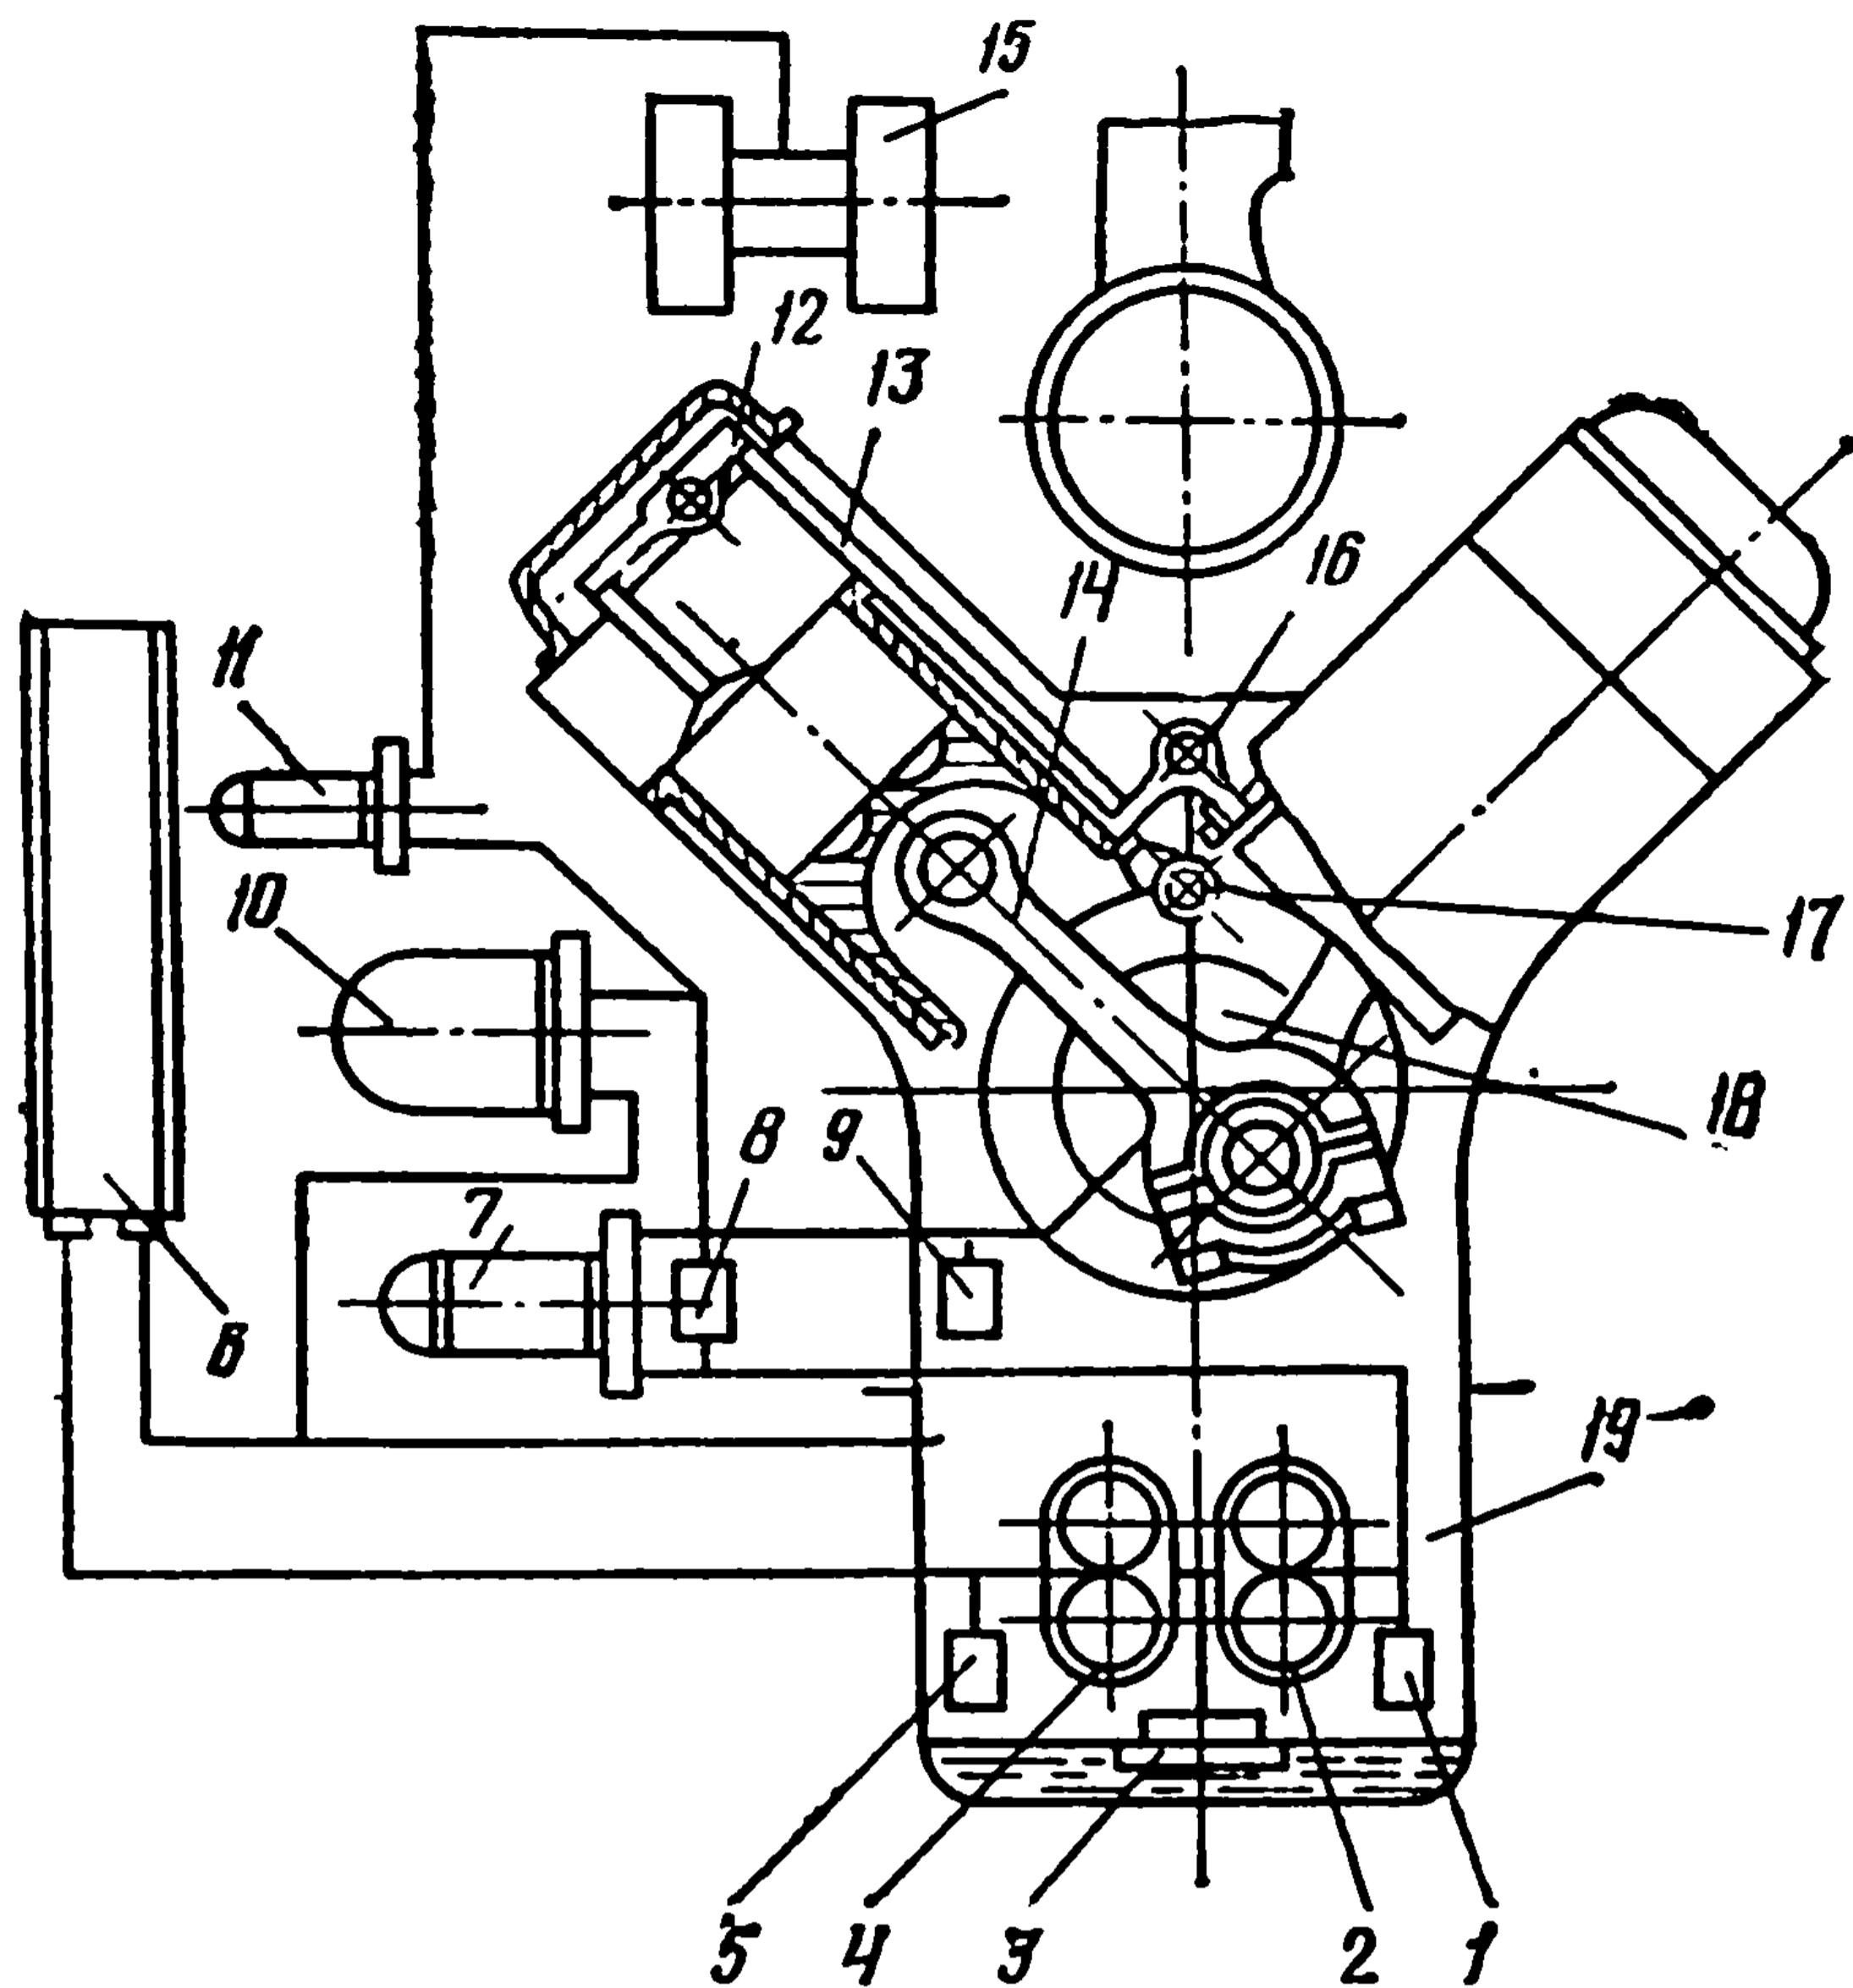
Схема смазочной системы дизеля ЯМЗ-238НБ:
